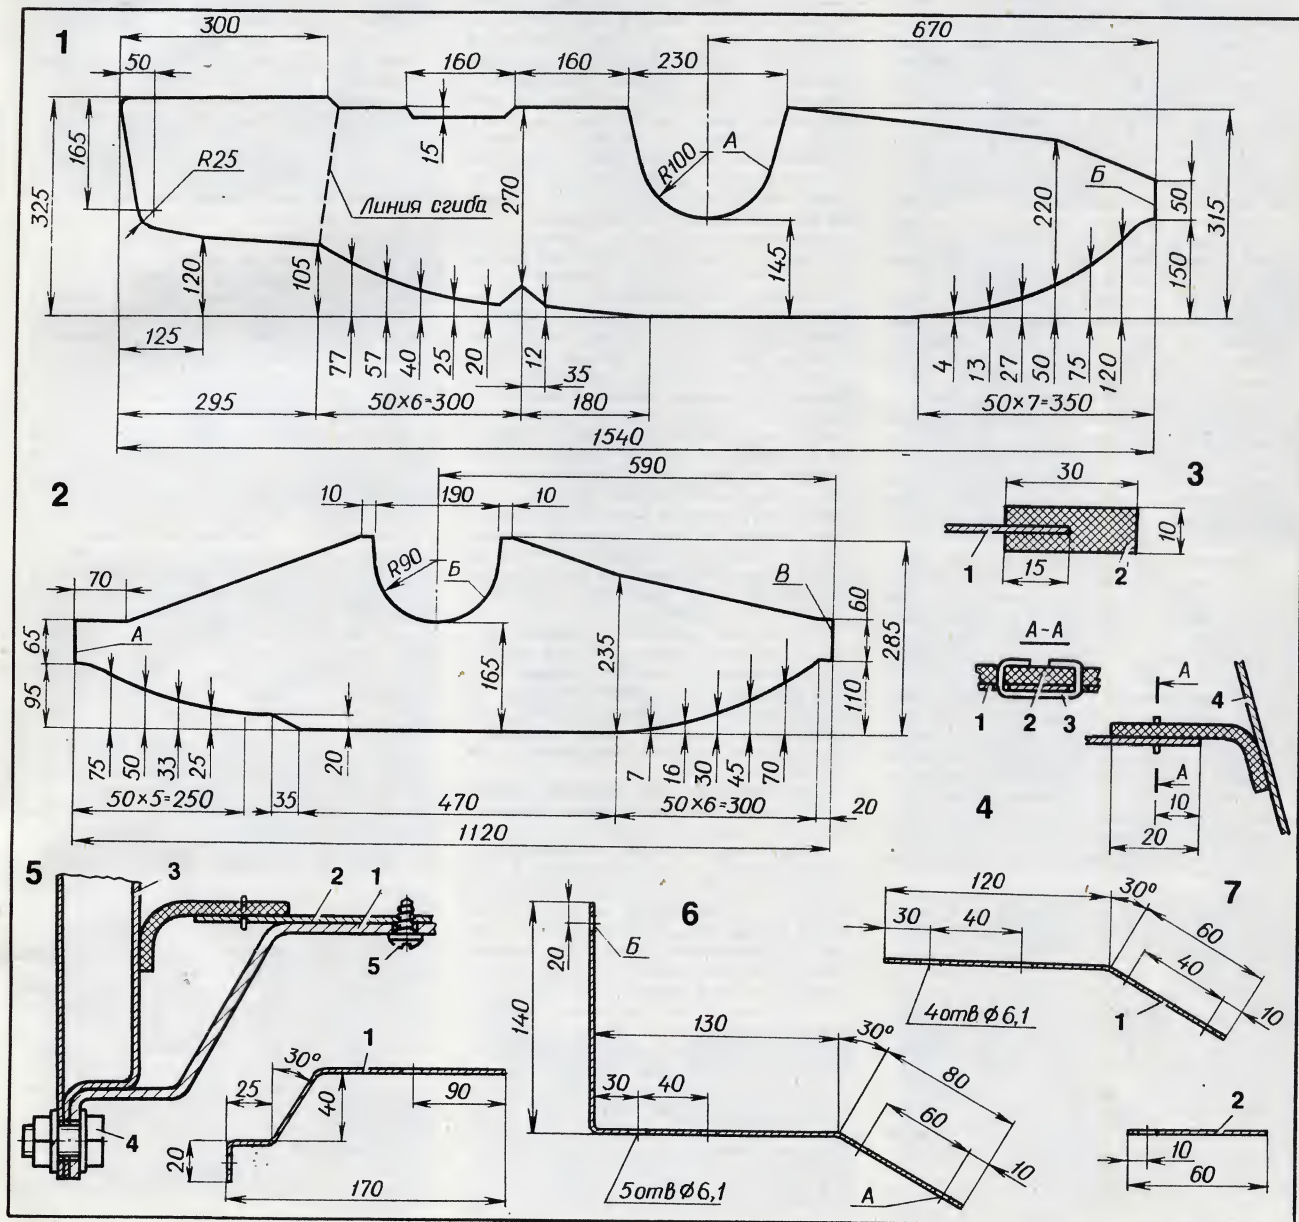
Окантовка щитка микропористой резиной: 1 — щиток; 2 — лист резины.
